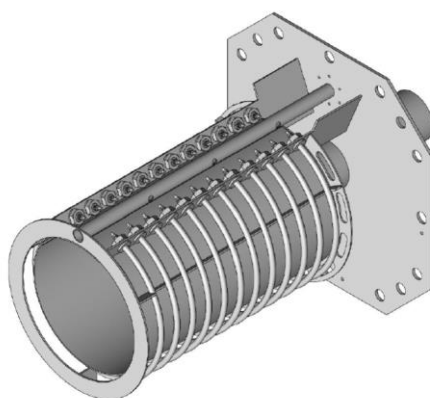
Внешний вид и устройство нагревателя электрического УОВ-НЭ
